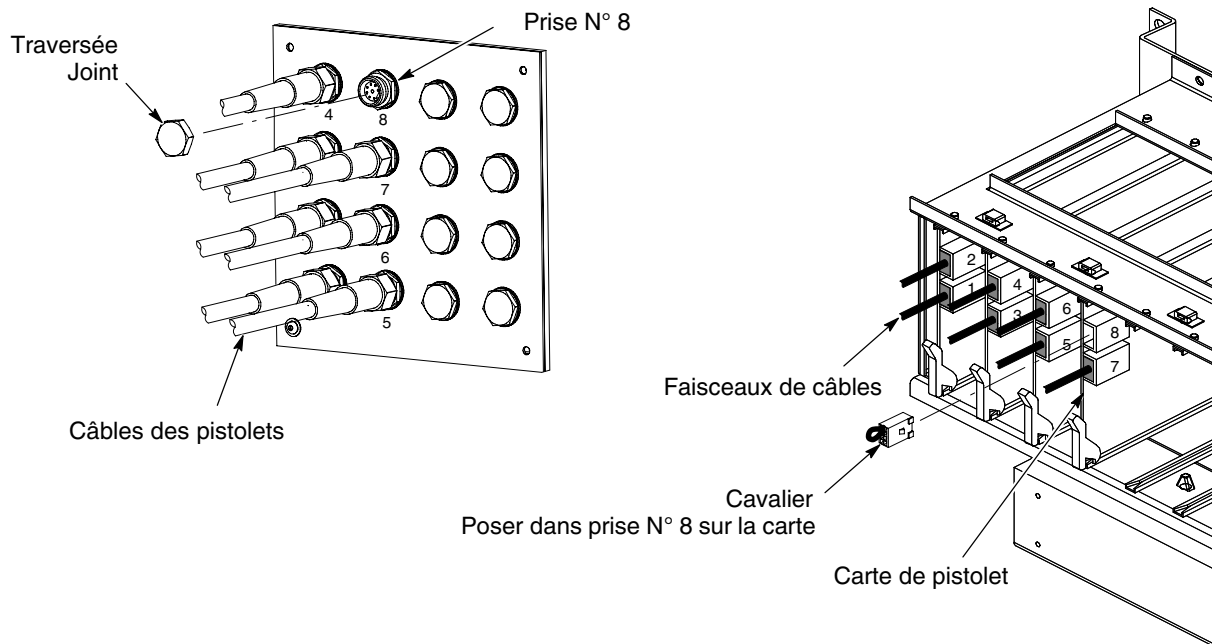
Pose du bouchon et du cavalier - Exemple illustrant un système à 8 pistolets utilisant 7 pistolets
